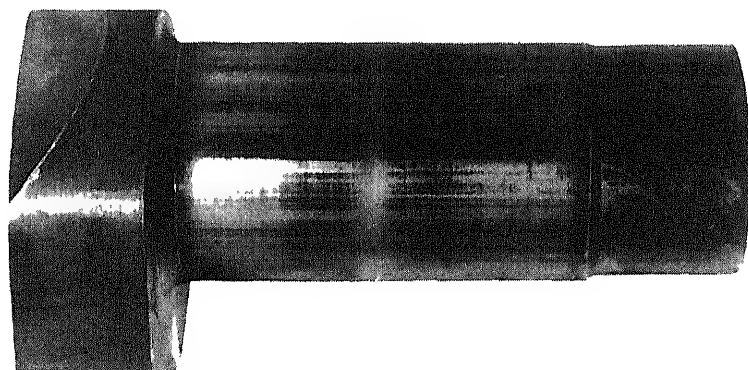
Шейка коленчатого вала с волнистой поверхностью
